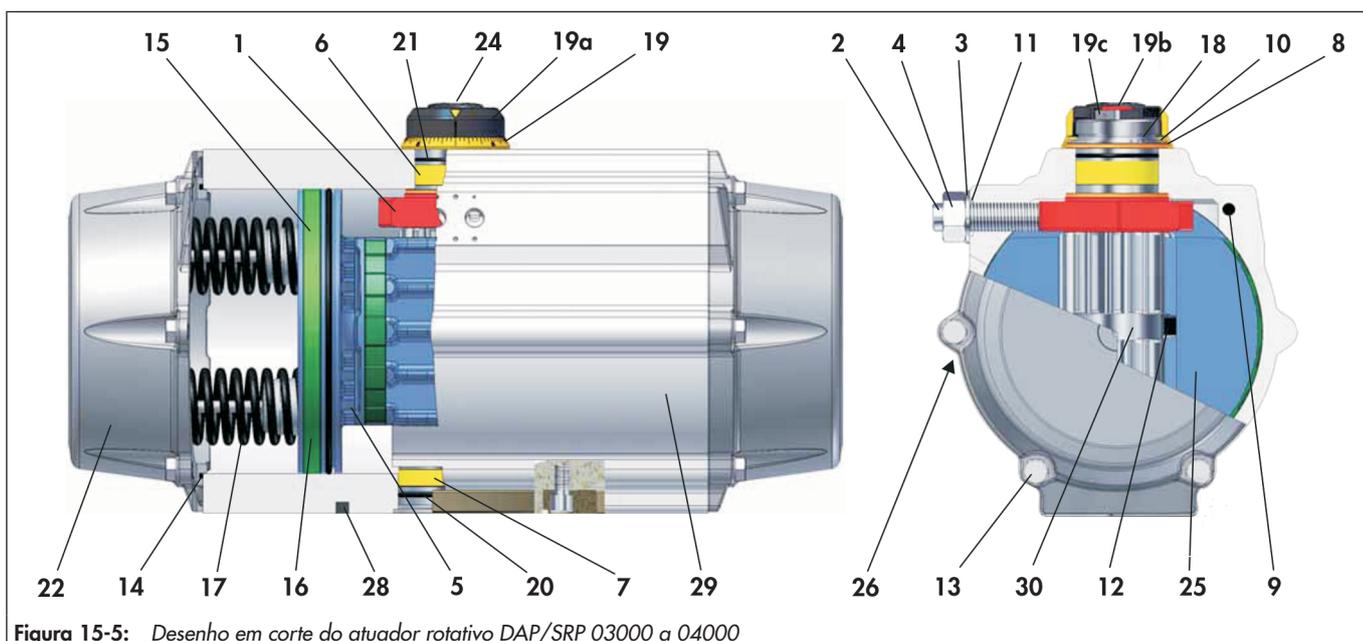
Desenho em corte do atuador rotativo DAP/SRP 03000 a 04000
